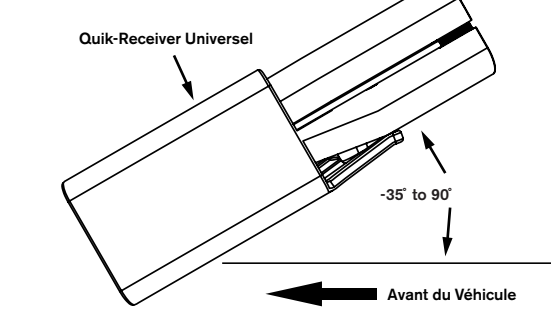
Angles de montage acceptables du G2 et du Quik-Receiver universel
